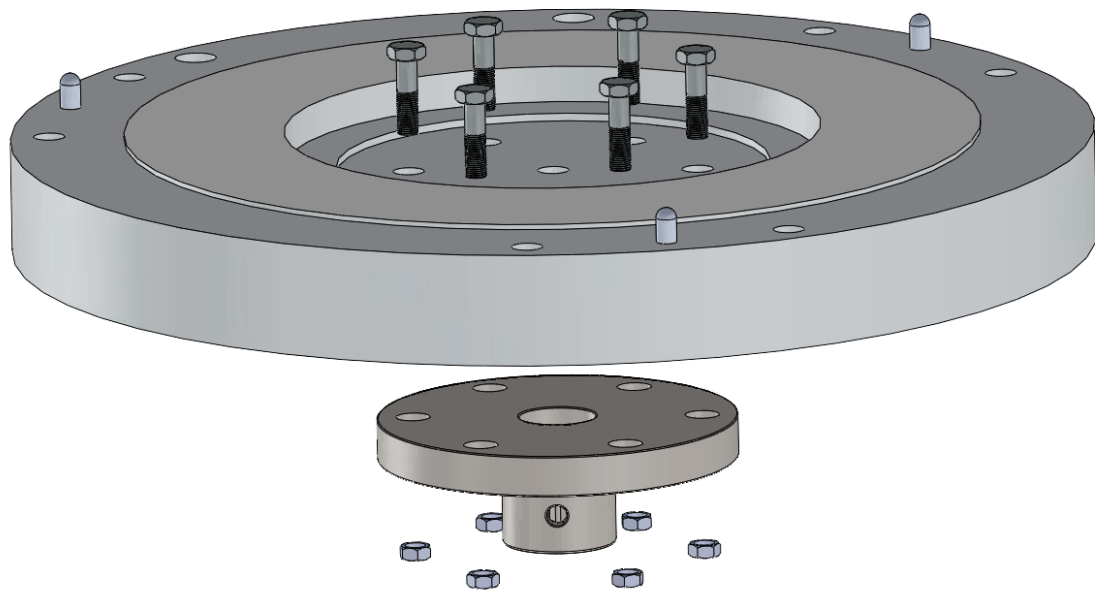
Vista explosionada de la unió de l'útil de fixació i el volant d'inèrcia.
